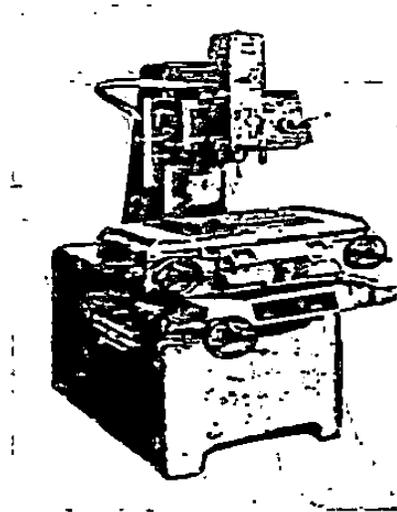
Mesin Bor Lantai Tipe Colum dan Pilar ⁽¹¹⁾
